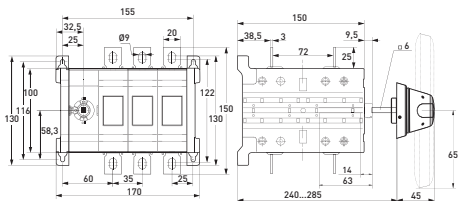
Габаритные и установочные размеры реверсивных рубильников 160-250А 3Р
